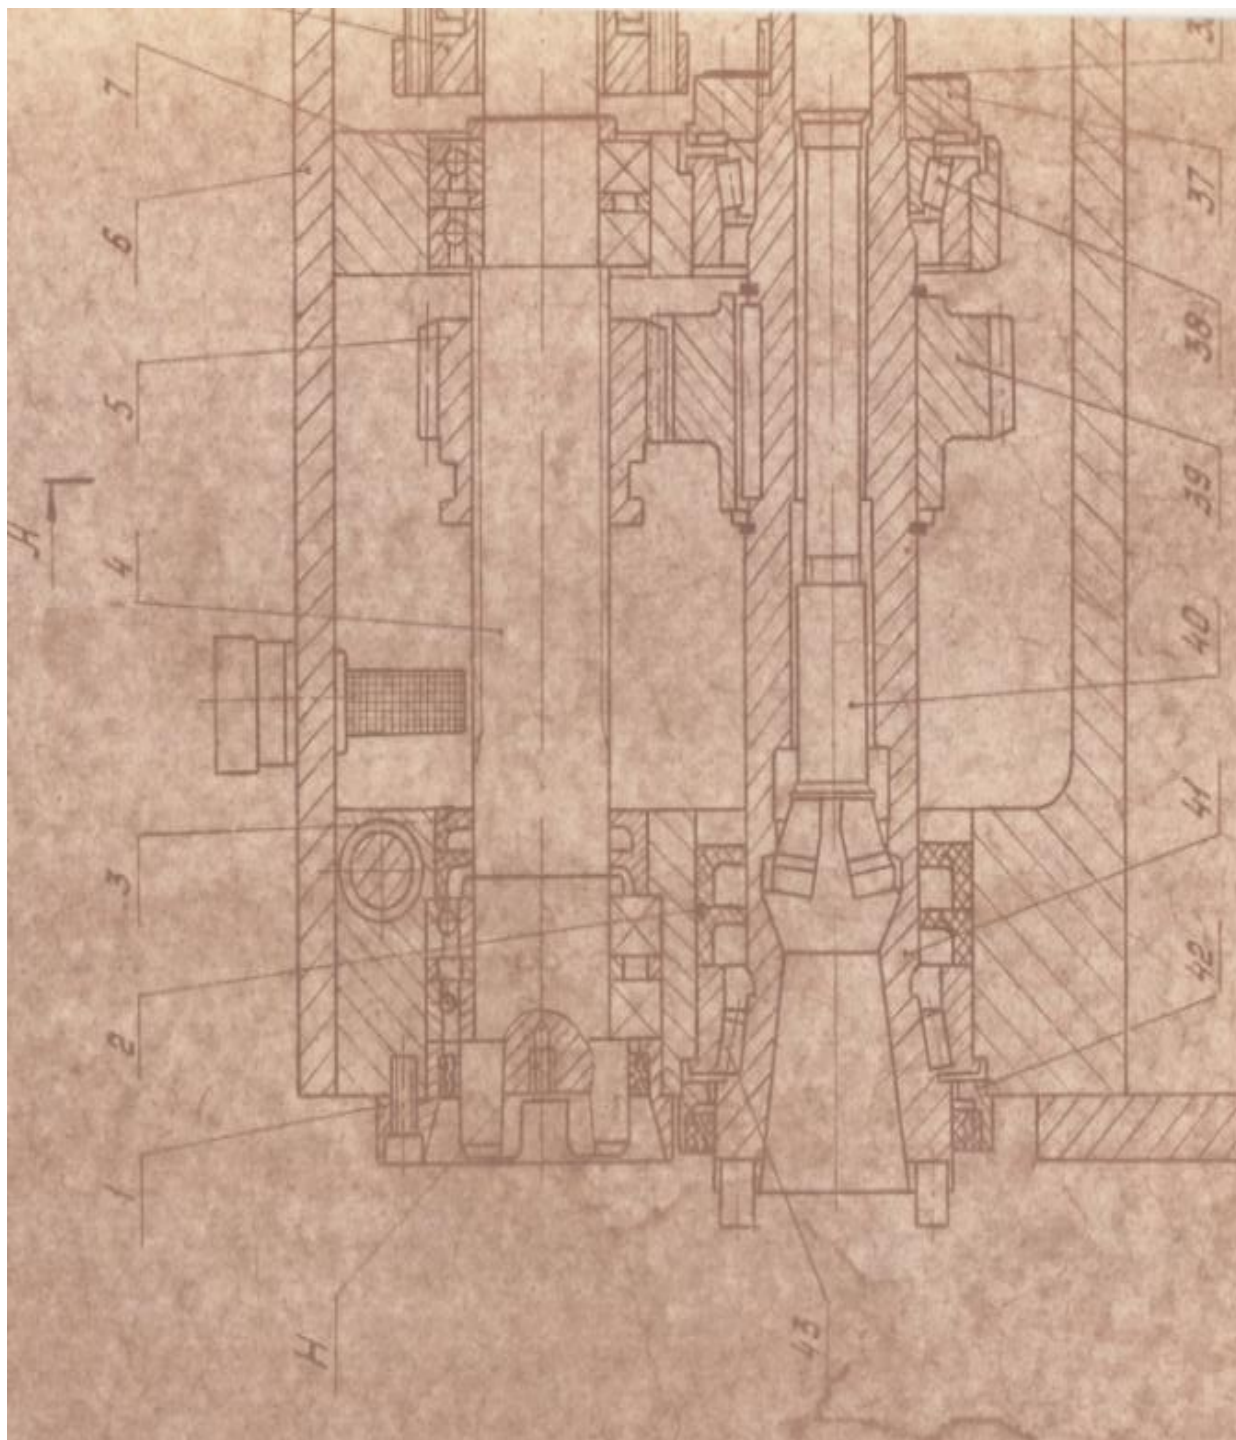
Горизонтальний шпиндельний вузол базового верстату
